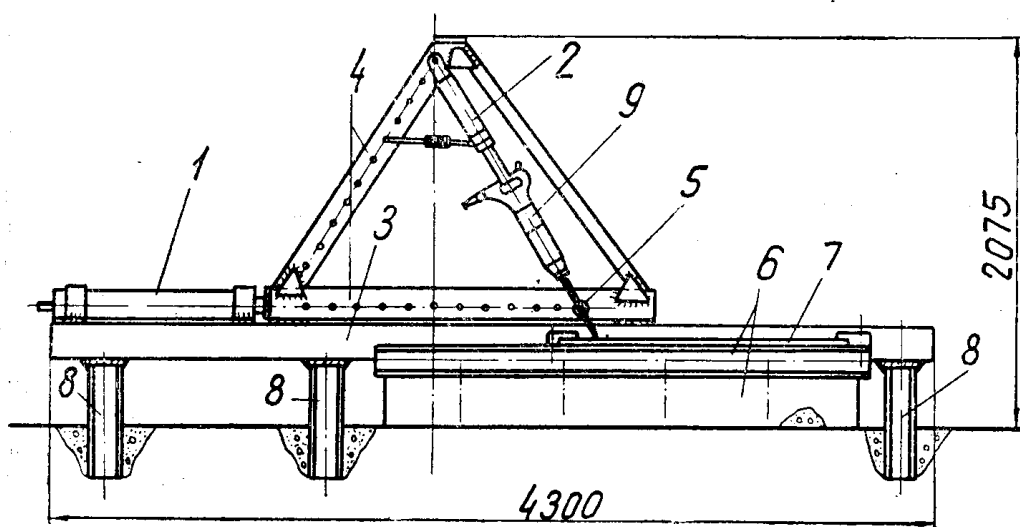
Схема стенда для исследования рубильно-клепальных молотков: 1 — пневмоподатчик для перемещения каретки; 2 — пневмоподатчик для создания усилия нажатия; 3 — направляющая рама; 4 — подвижная каретка; 5 — люнет; 6 — стол; 7 — заготовка; 8 — стойки; 9 — пневматический молоток.
